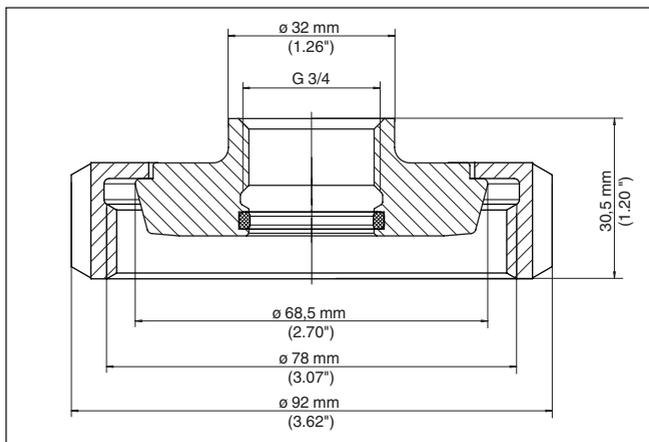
Dimensiones adaptador de rosca G $\frac{3}{4}$ (DIN 3852-X) a racor roscado DN 50 (DIN 11851) PN 25
